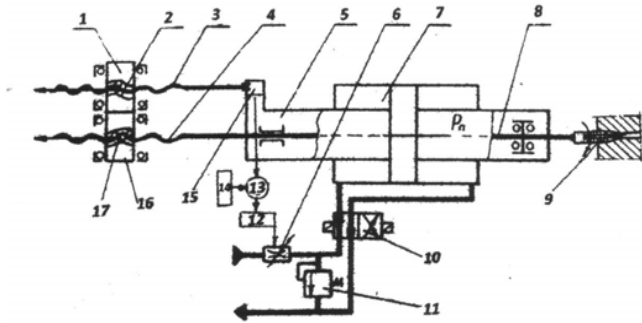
Схема передаточного механізму і перетворювача поступального руху в гвинтовій рух формоутворення гвинторізних верстатів
